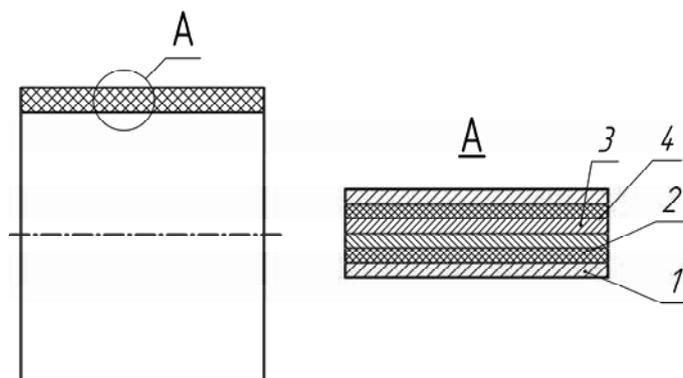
Конструкция оплеточного рукава: 1 – резиновый слой; 2 – хлопчатобумажная оплетка; 3 – металлическая оплетка; 4 – специальная паста
